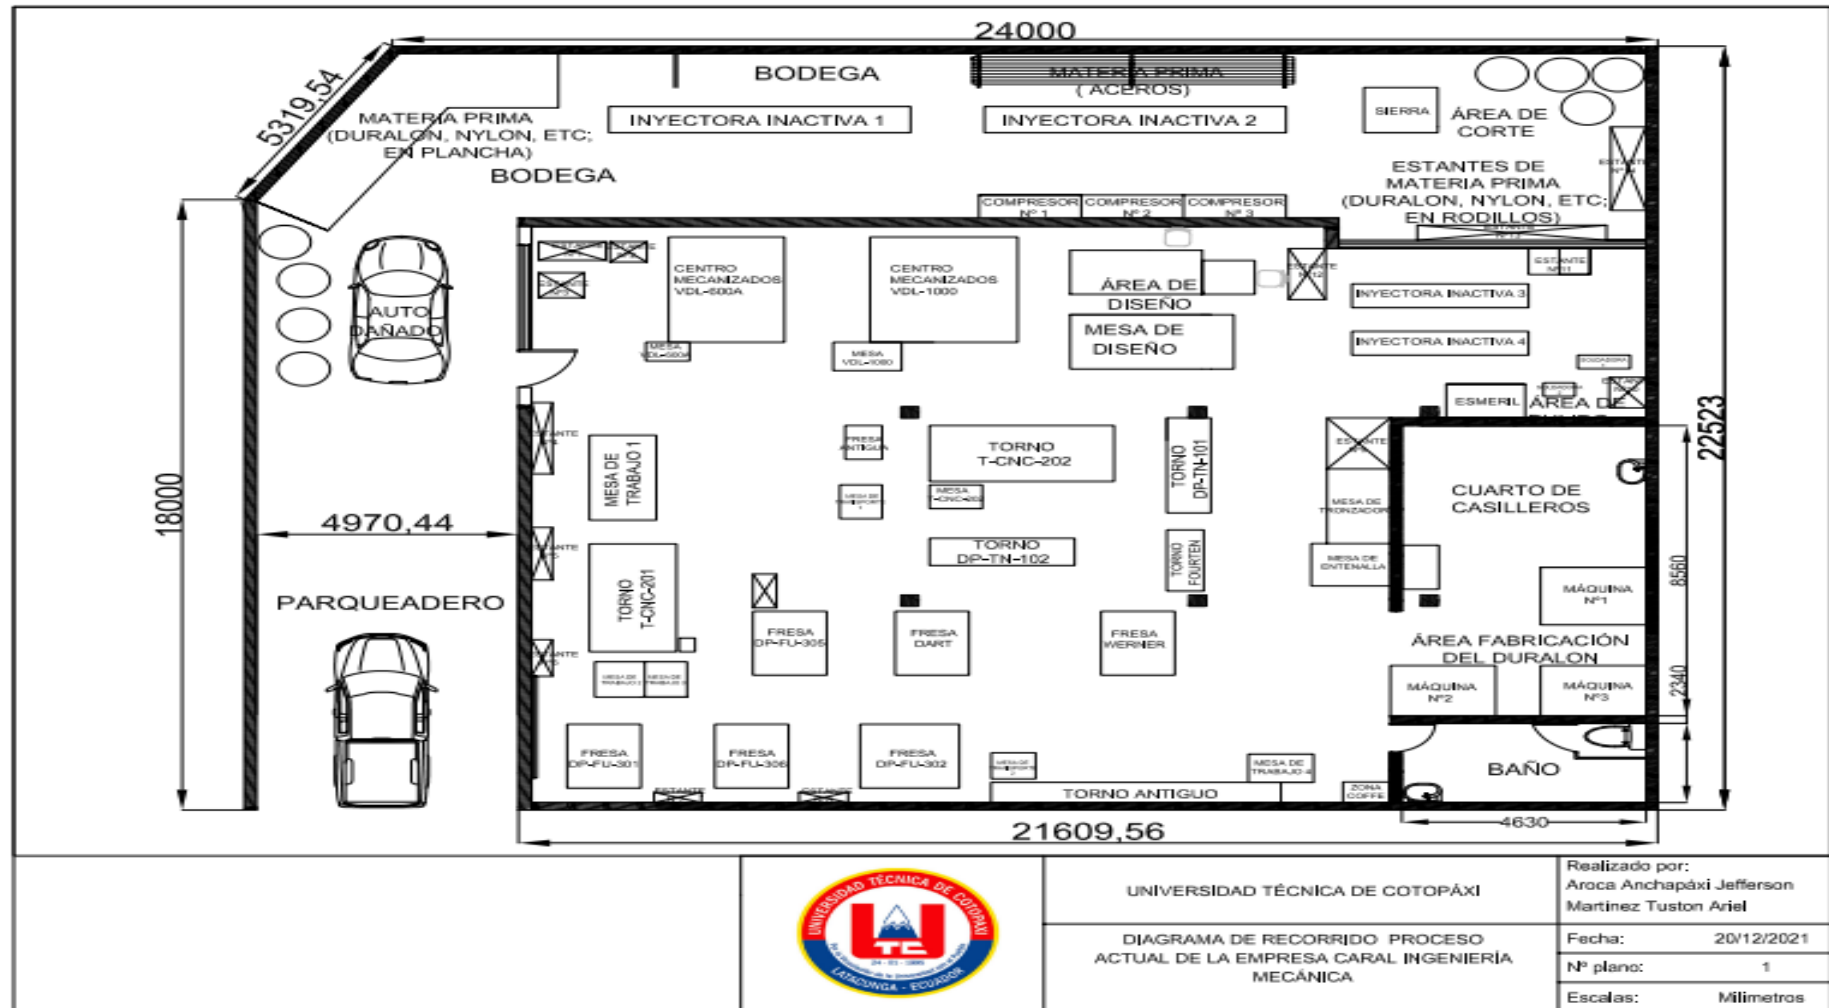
Layout de la empresa “Caral Ingeniería Mecánica”.
